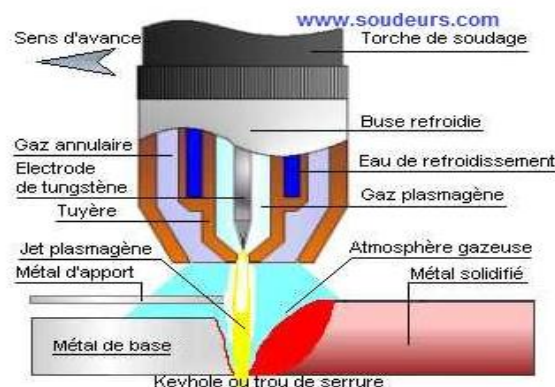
Principe de Soudage à l'arc plasma [15]
